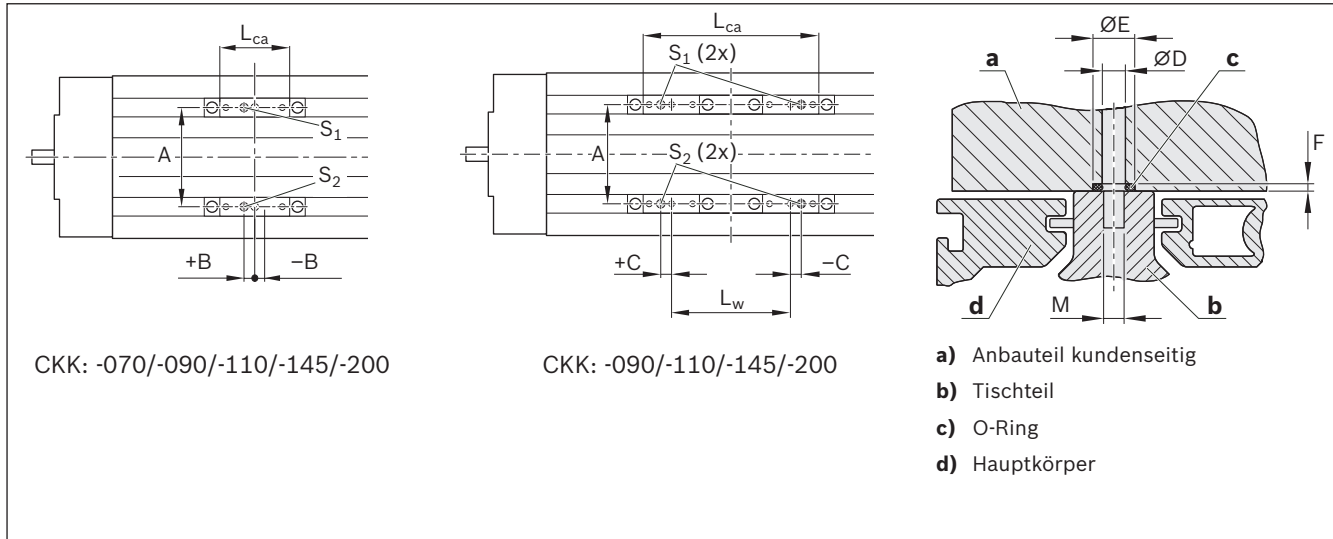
Lage der Schmierbohrungen Im Tischteil (CKK)
